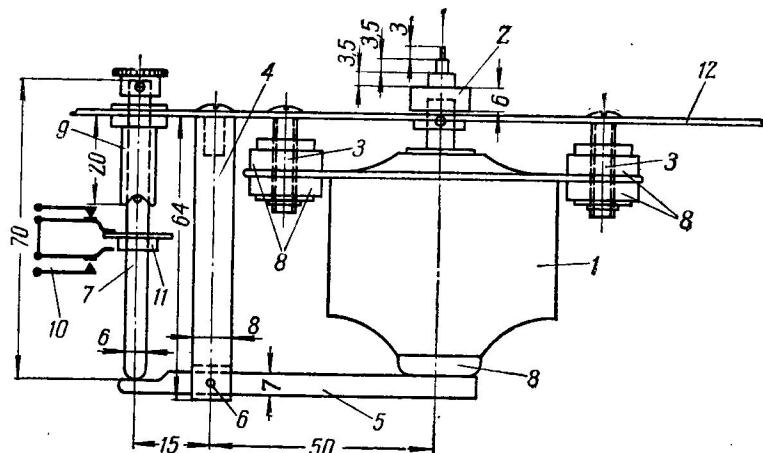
Внутреннее устройство проигрывателя: 1 — двигатель; 2 — четырехступенчатая насадка; 3 — скользящие муфты; 4 — стойка рычага; 5 — рычаг; 6 — ось поворота рычага; 7 — штифт с поворотной кнопкой; 8 — резиновый амортизатор; 9 — втулка штифта; 10 — контактная группа; 11 — текстолитовый диск; 12 — металлическая панель проигрывателя.
